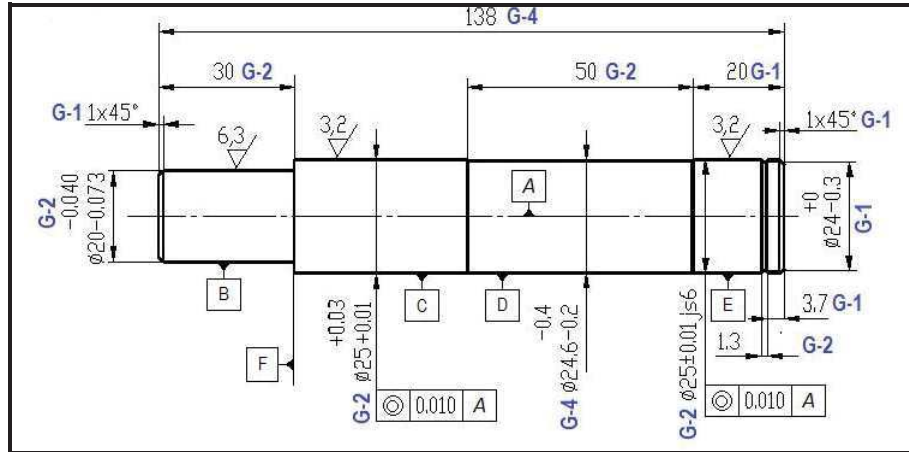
Representación de la descripción dimensional del eje 2 perteneciente al conjunto del rodillo vertical, más los grupos dimensionales de cada una de las dimensiones.
